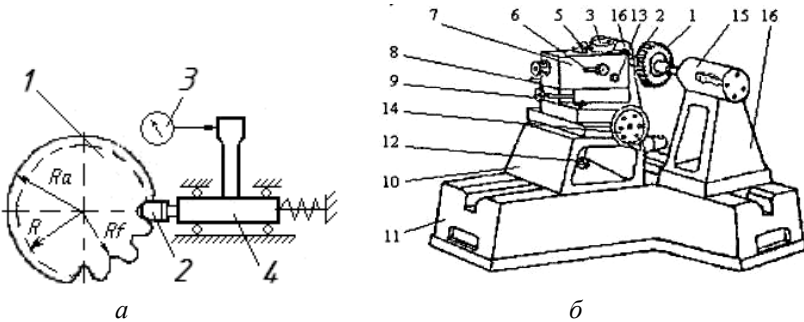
Биттємір Б-10м: а – схема вимірювання; б – загальний вид.
